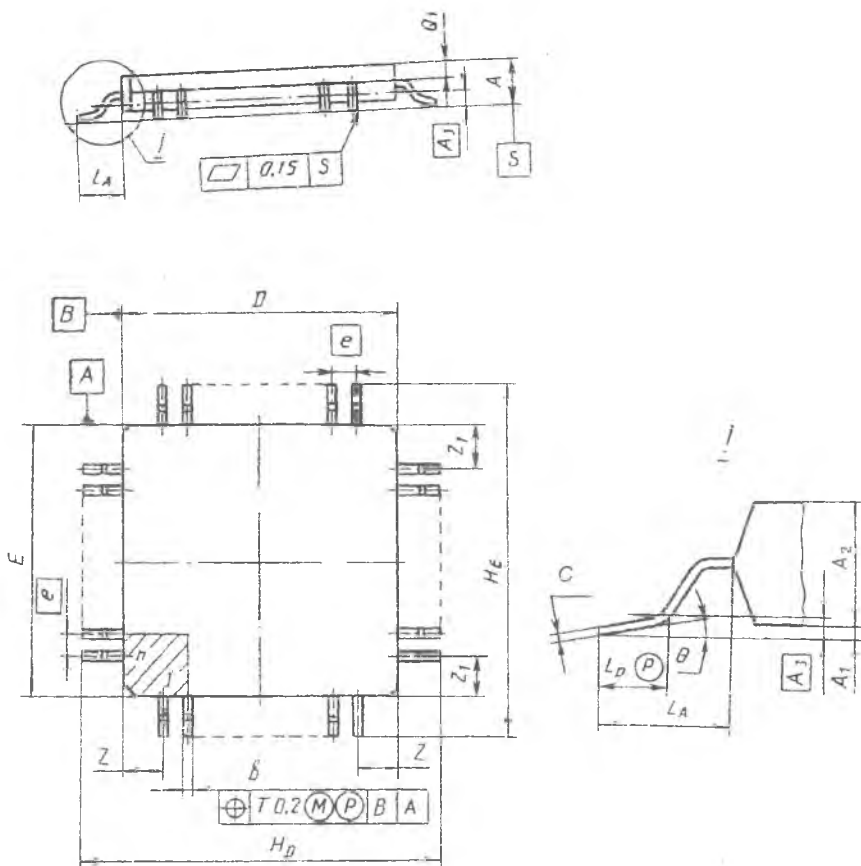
Конструкция корпуса типа 4 подтипа 4
